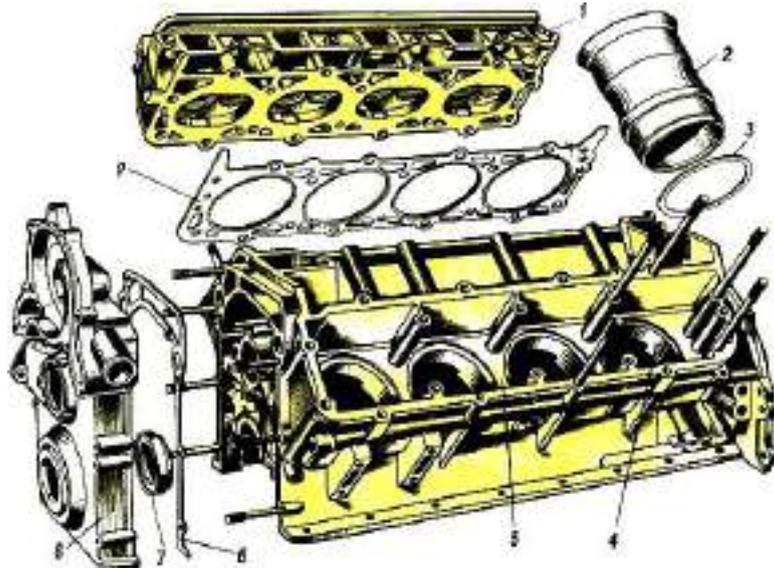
Головка и блок цилиндров V-образного восьмицилиндрового двигателя: 1 – головка цилиндров; 2 – гильза цилиндров; 3 – прокладка гильзы; 4 – направляющий пояс для гильзы; 5 – блок цилиндров; 6 – прокладка передней крышки; 7 – сальник; 8 – передняя крышка; 9 – прокладка головки цилиндров
